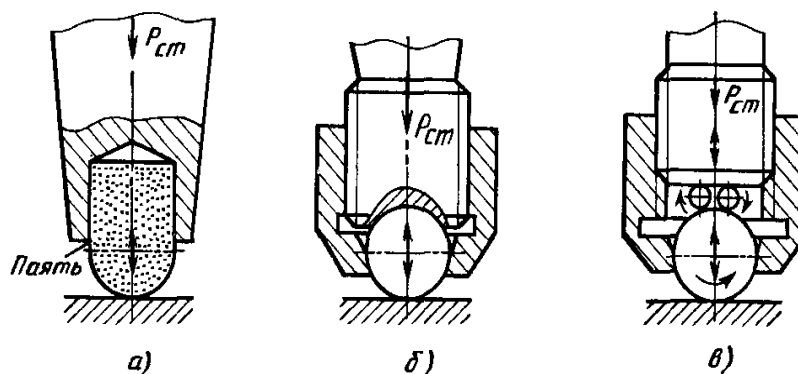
Варианты крепления рабочей части инструмента:
